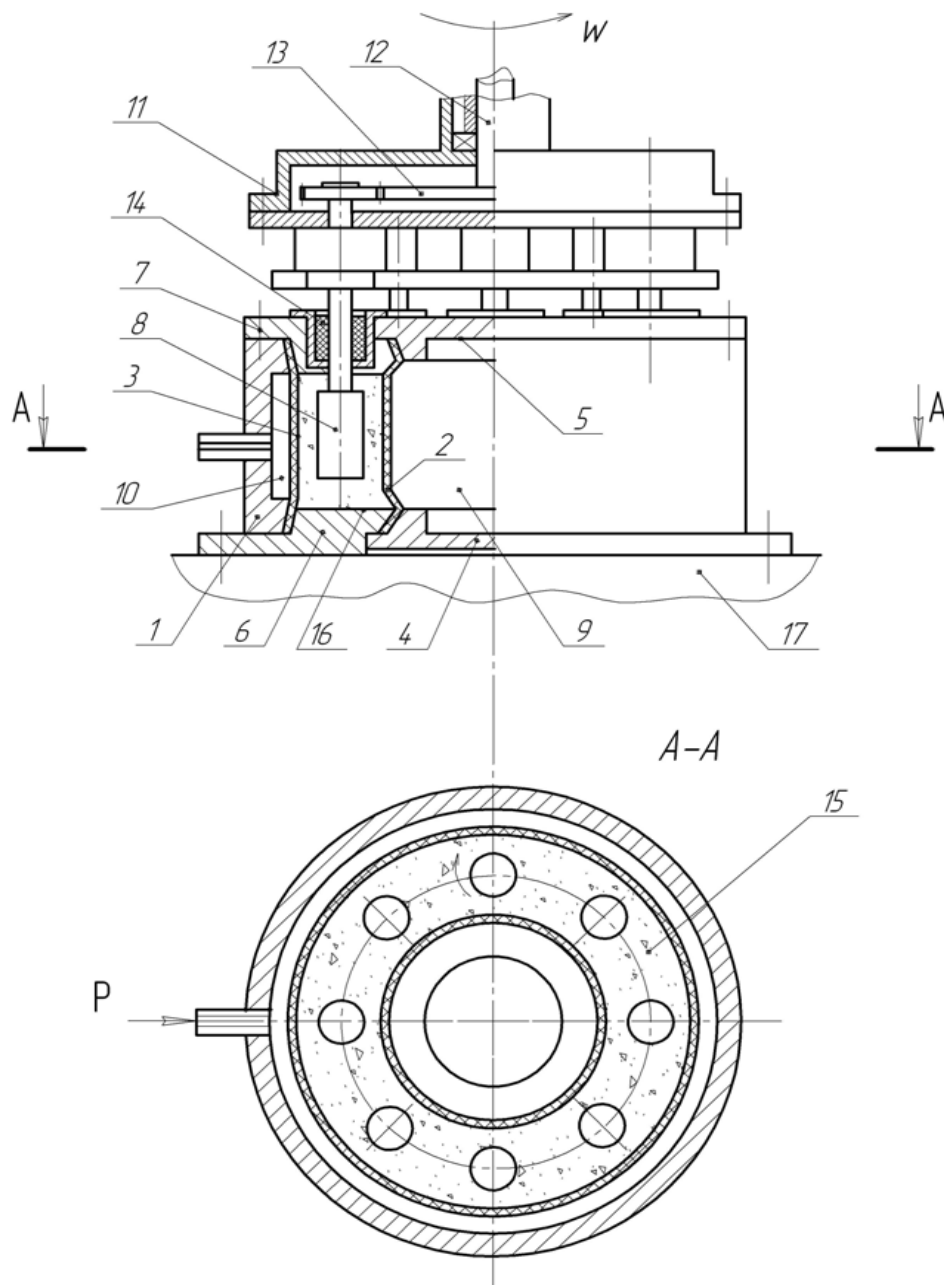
Схема пристрою для обробки деталей сферичної форми
